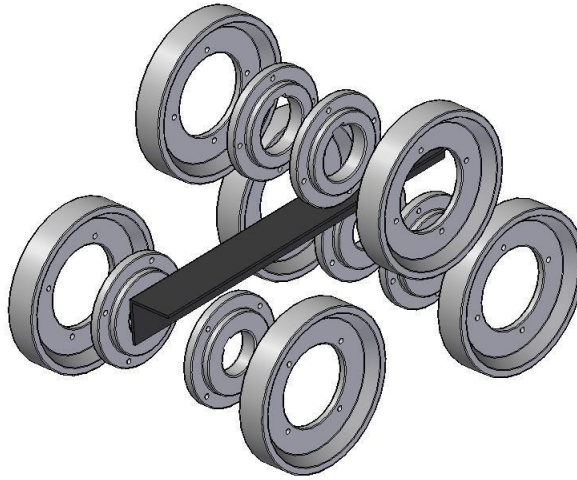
Disposición de matrices para perfil ángulo explosionada.
